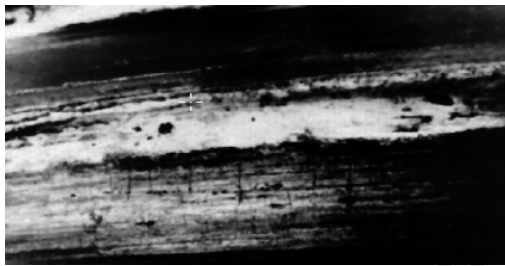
Fisuras térmicas en el centro de la rodadura
